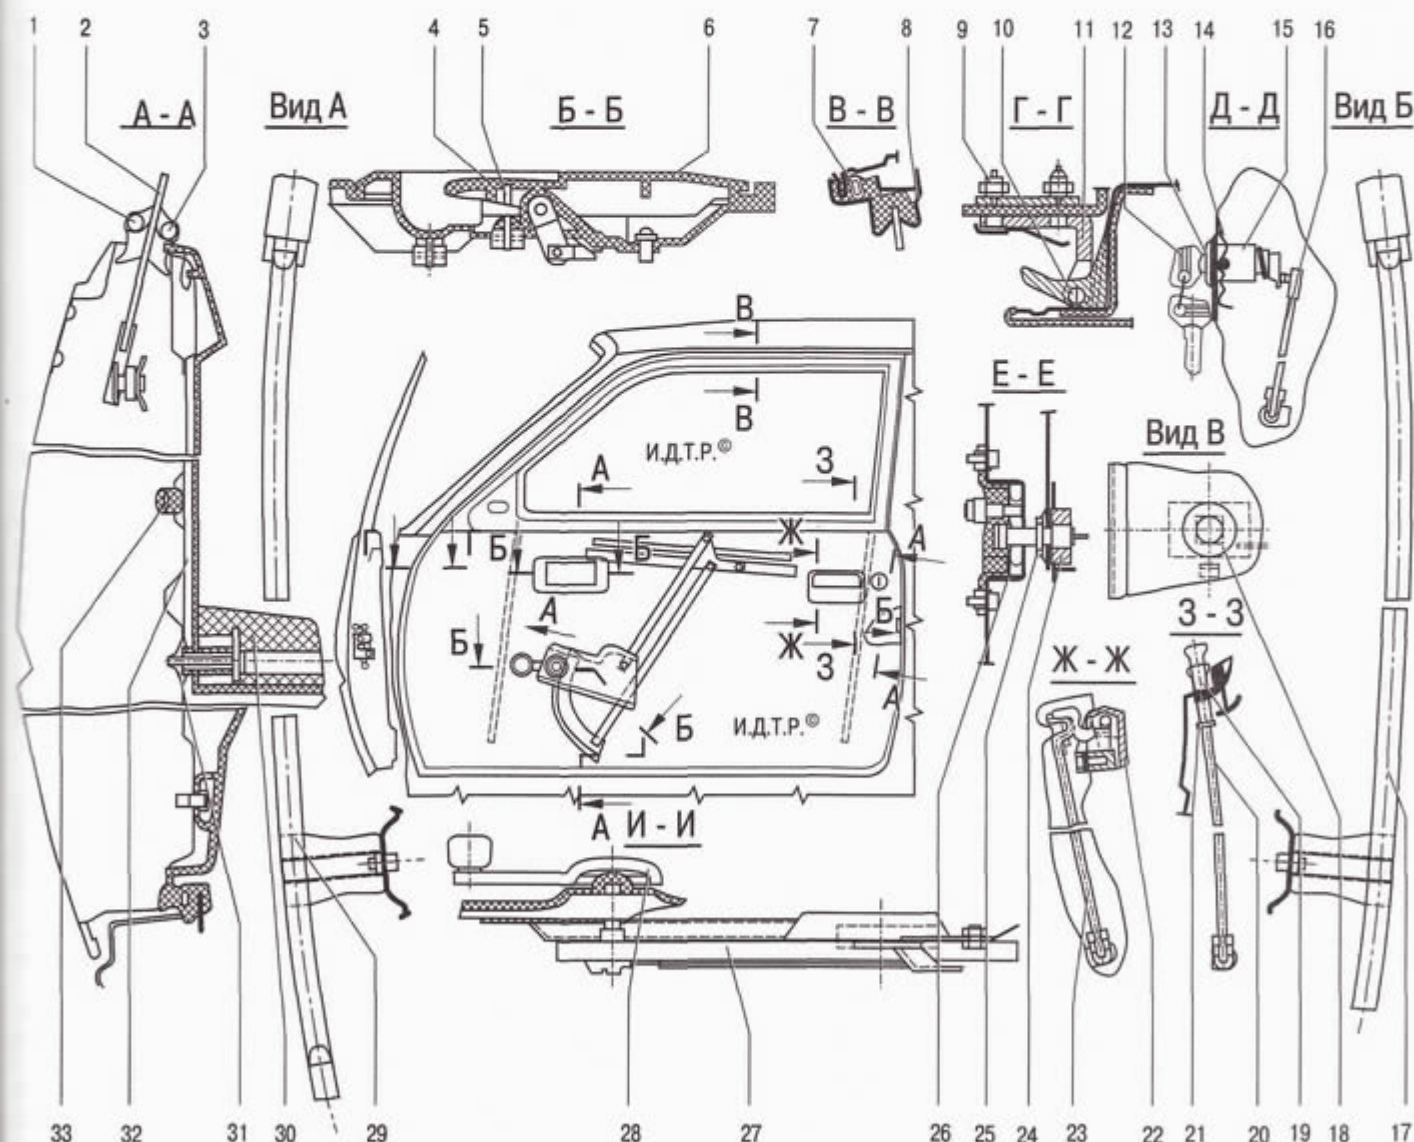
Передняя дверь: 1 – наружный подоконный уплотнитель; 2 – опускающее стекло; 3 – внутренний подоконный уплотнитель; 4 – внутренняя ручка; 5 – заглушка ручки; 6 – облицовка внутренней ручки; 7 – вставка уплотнителя двери; 8 – уплотнитель стекла; 9 – гайка; 10 – ось петли; 11 – петля; 12 – ключи замка двери; 13 – уплотнитель выключателя; 14 – скоба крепления выключателя; 15 – выключатель замка; 16 – тяга выключателя; 17 – правая стойка; 18 – шайба фиксатора замка; 19 – кнопка; 20 – тяга; 21 – розетка; 22 – наружная ручка двери; 23 – тяга привода наружной ручки; 24 – пластина фиксатора; 25 – фиксатор замка; 26 – замок двери; 27 – стеклоподъемник в сборе; 28 – ручка стеклоподъемника; 29 – левая стойка; 30 – подлокотник; 31 – пластинчатая гайка; 32 – обивка двери; 33 – держатель тяги
